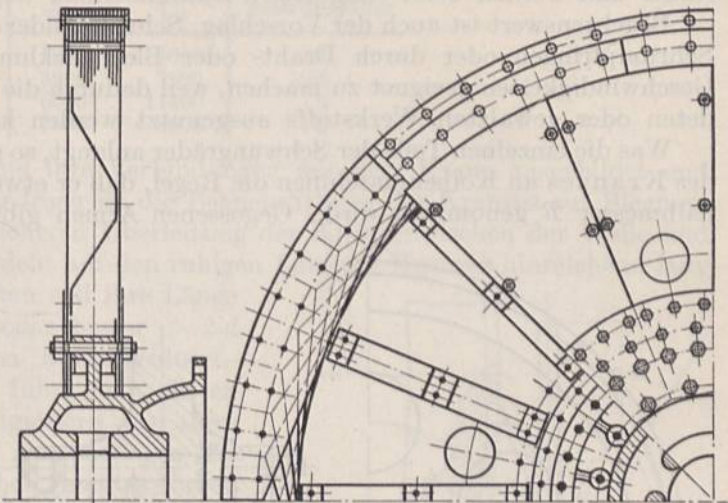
Schwungrad einer Walzenzugmaschine aus Blechplatten.
